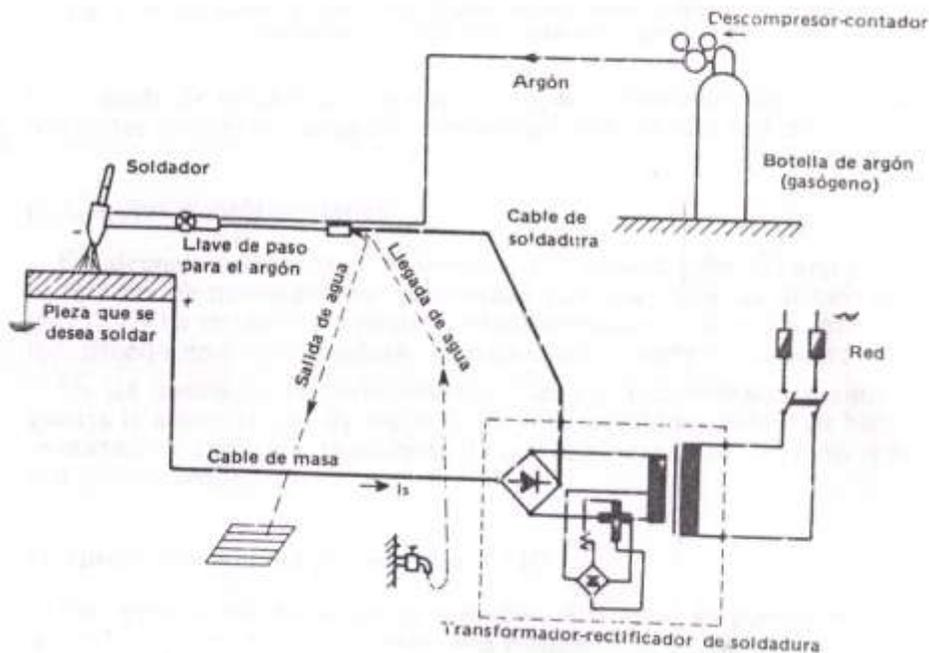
Instalación de soldadura TIG con transformador-rectificador de soldadura.
